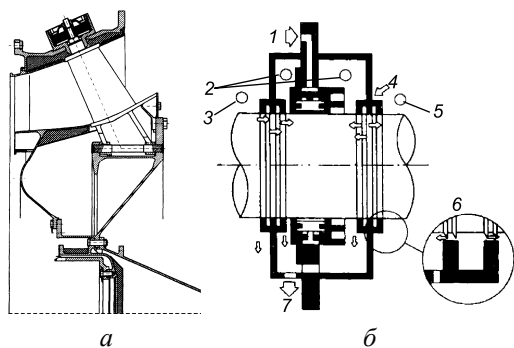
Конструкция опорного венца ТНД (а) [9] и схема смазки и уплотнения узла подшипника ГТУ GT35 (б) [15]:
